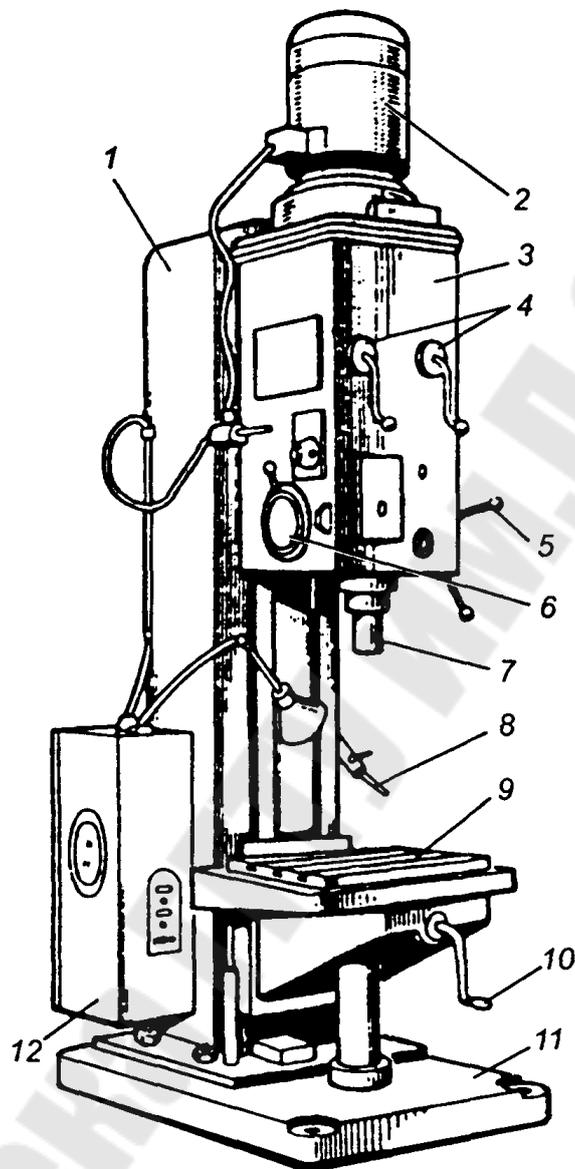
Общий вид вертикально-сверильного станка
